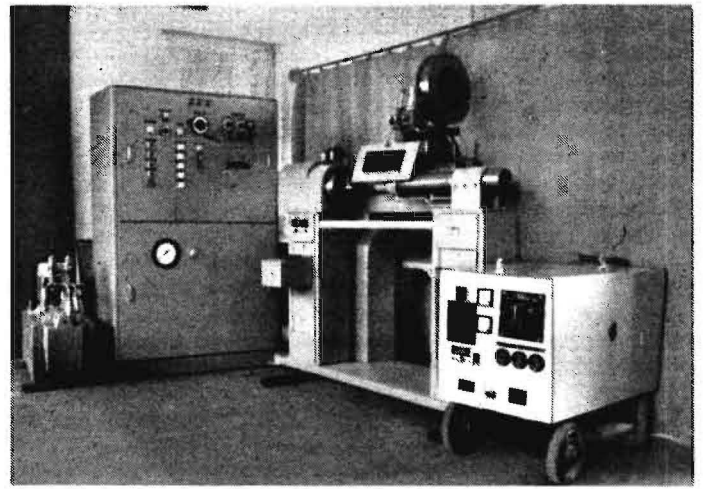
MAG-Schweißmaschine SM-03/K. bestehend aus Grundschweißgerät, Steuerschrank für Elektrik und Hydraulik sowie Schweißstromquelle RGS 315/1)
